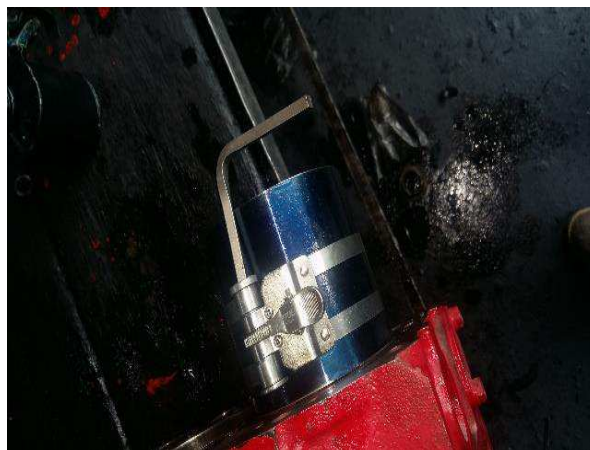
Montaje del conjunto pistón biela del motor Hino 205
